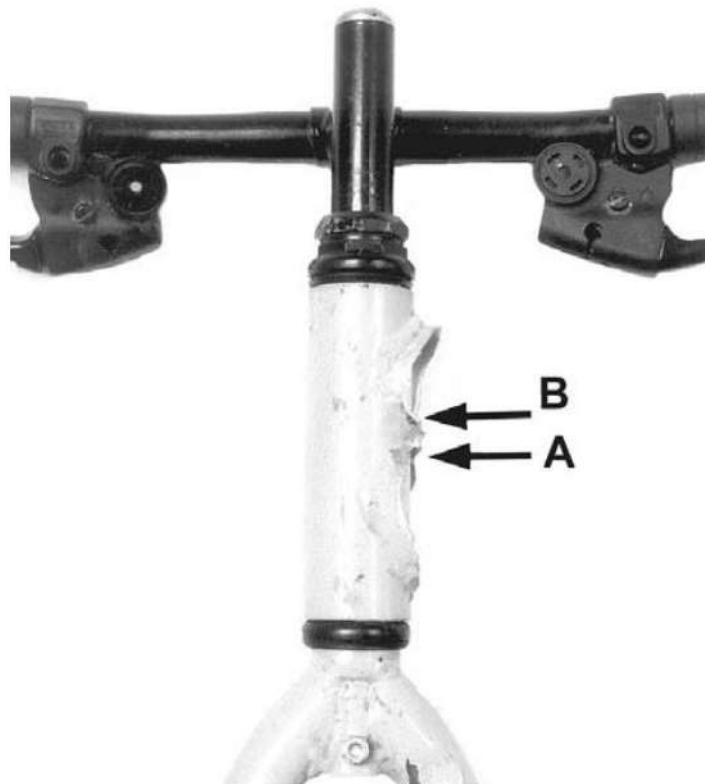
Detalle de la región fracturada del tubo 3, evidenciando que la rotura ocurrió en la soldadura de unión de los tubos. Las flechas A y B apuntan para los locales de inicio de la fractura.
